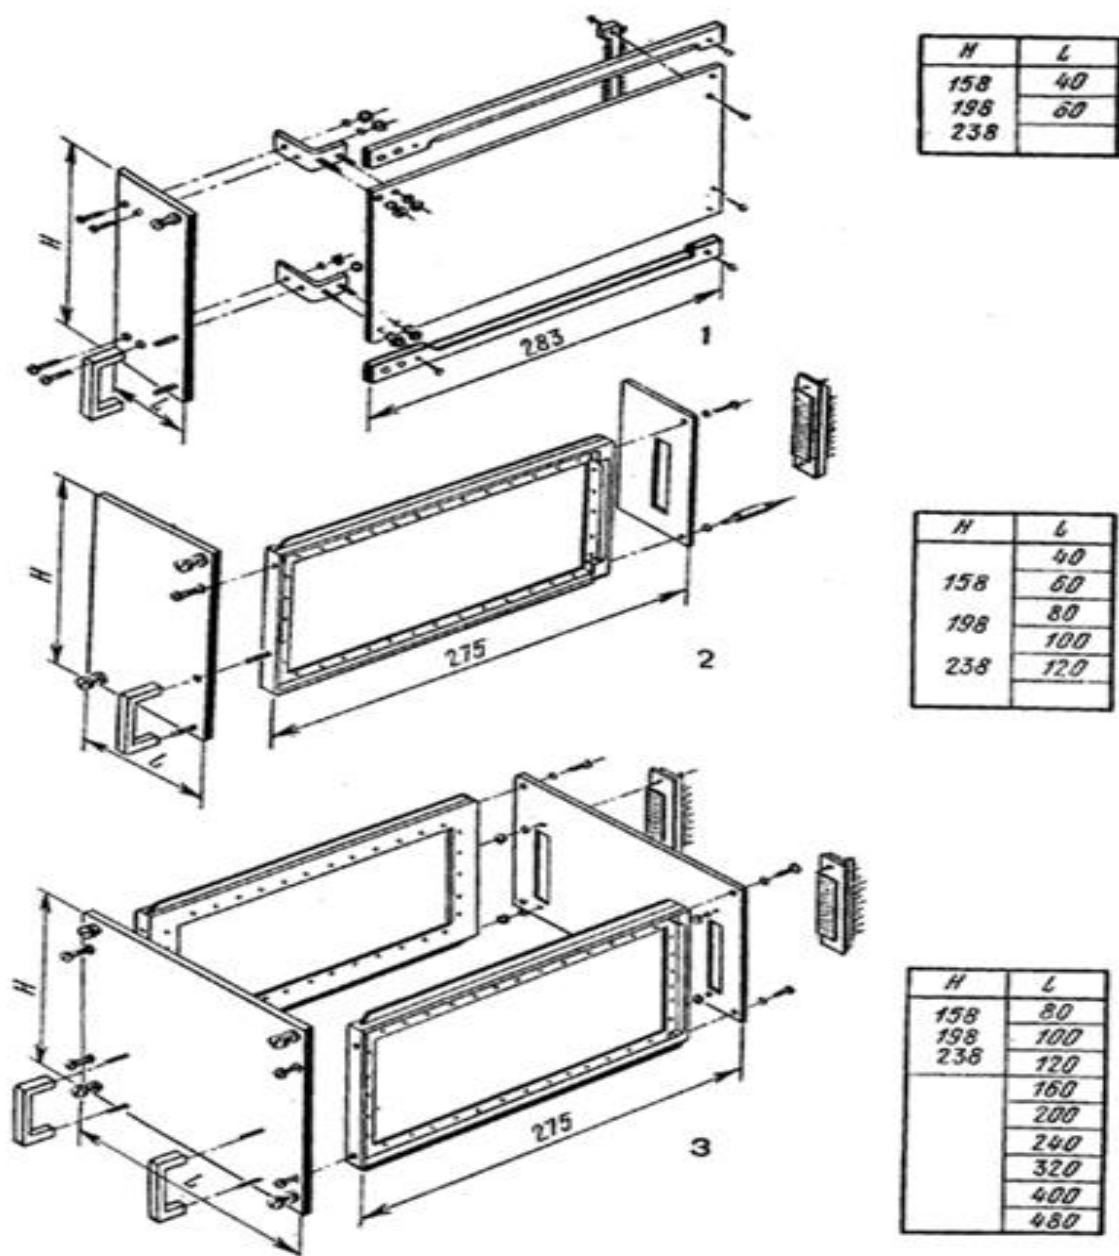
Схема конструкций частичных корпусов комплекса универсальных типовых конструкций УТК РЭС [ 5]
